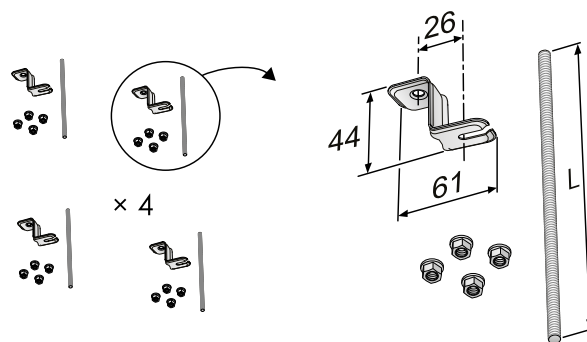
Élément d'assemblage SYST MS M8-1, montage au plafond et sur tige filetée
